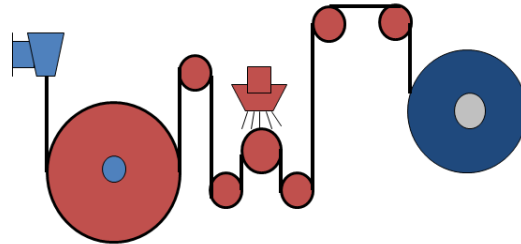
Rodillos integrados a una extrusora.
